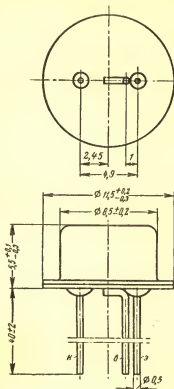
Габаритный чертеж транзисторов П101—П103.
